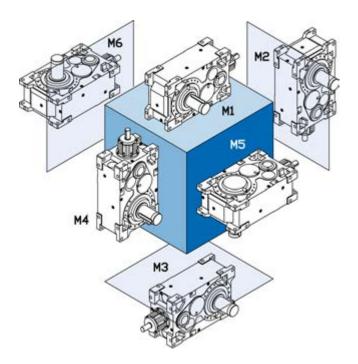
Монтажные положения конических редукторов со стандартными монтажными поверхностями
